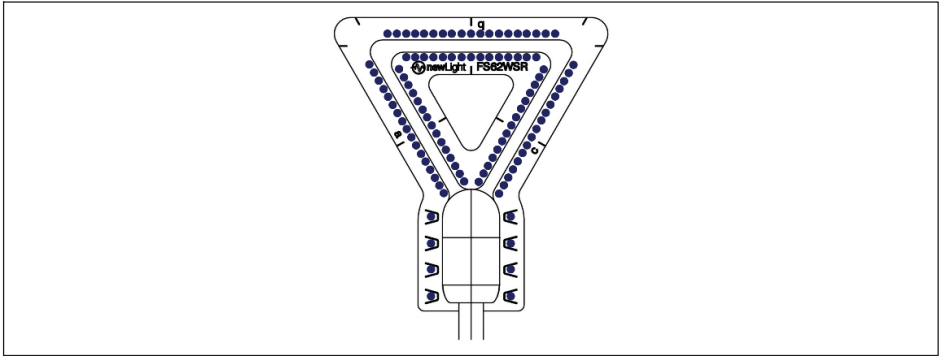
Schweißreihenfolge für die Rosette FS62WSR, Schritt 3
